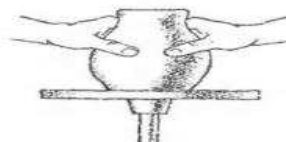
Расположение рук гончара при создании формы шейки кувшина
